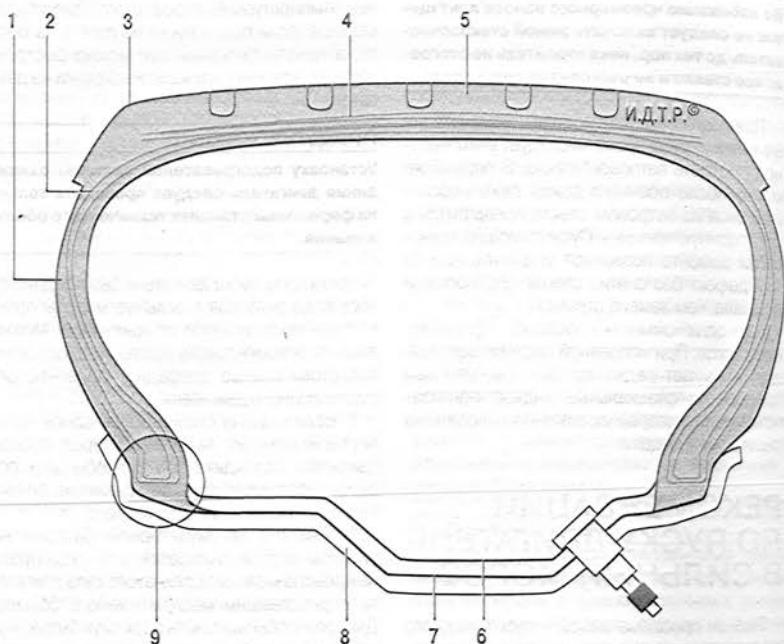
Элементы конструкции шины: 1 – боковина; 2 – каркас; 3 – плечевая зона; 4 – брекер; 5 – протектор; 6 – камера; 7 – ободная лента; 8 – обод; 9 – борт
